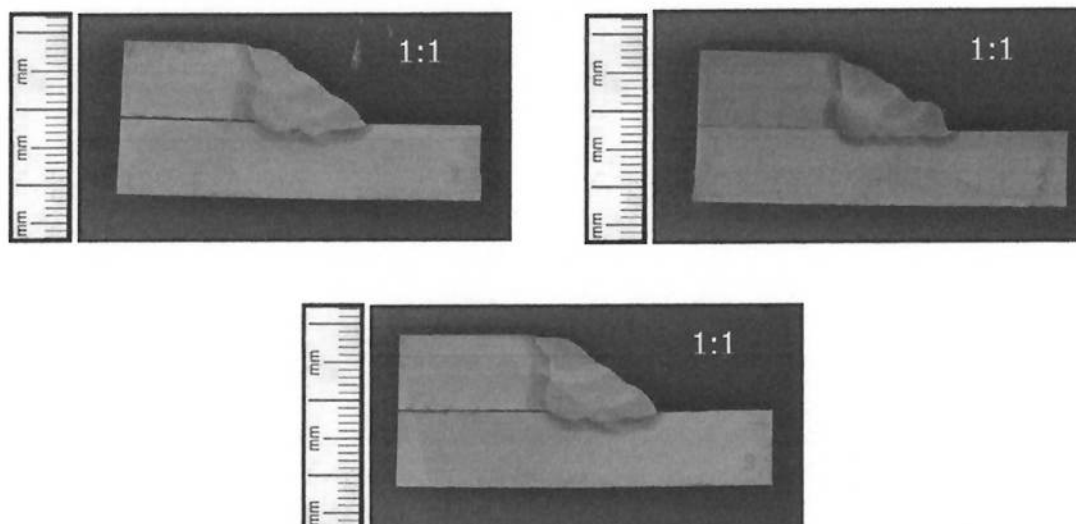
Ensaio de macrografia da junta soldada com energia de soldagem intermediária (1,05 kJ/mm).
